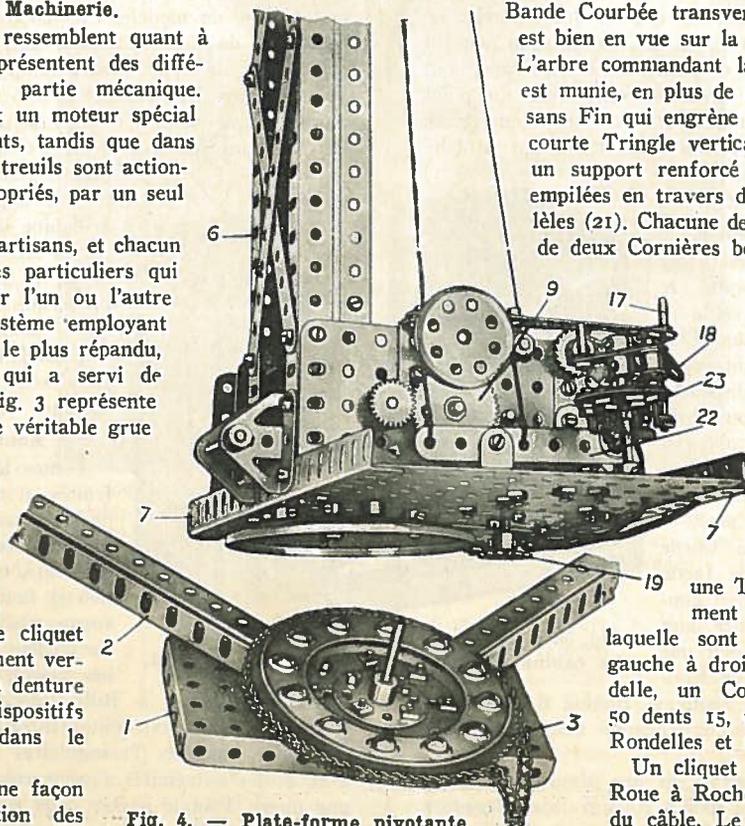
Plate-forme pivotante et machinerie du modèle.
